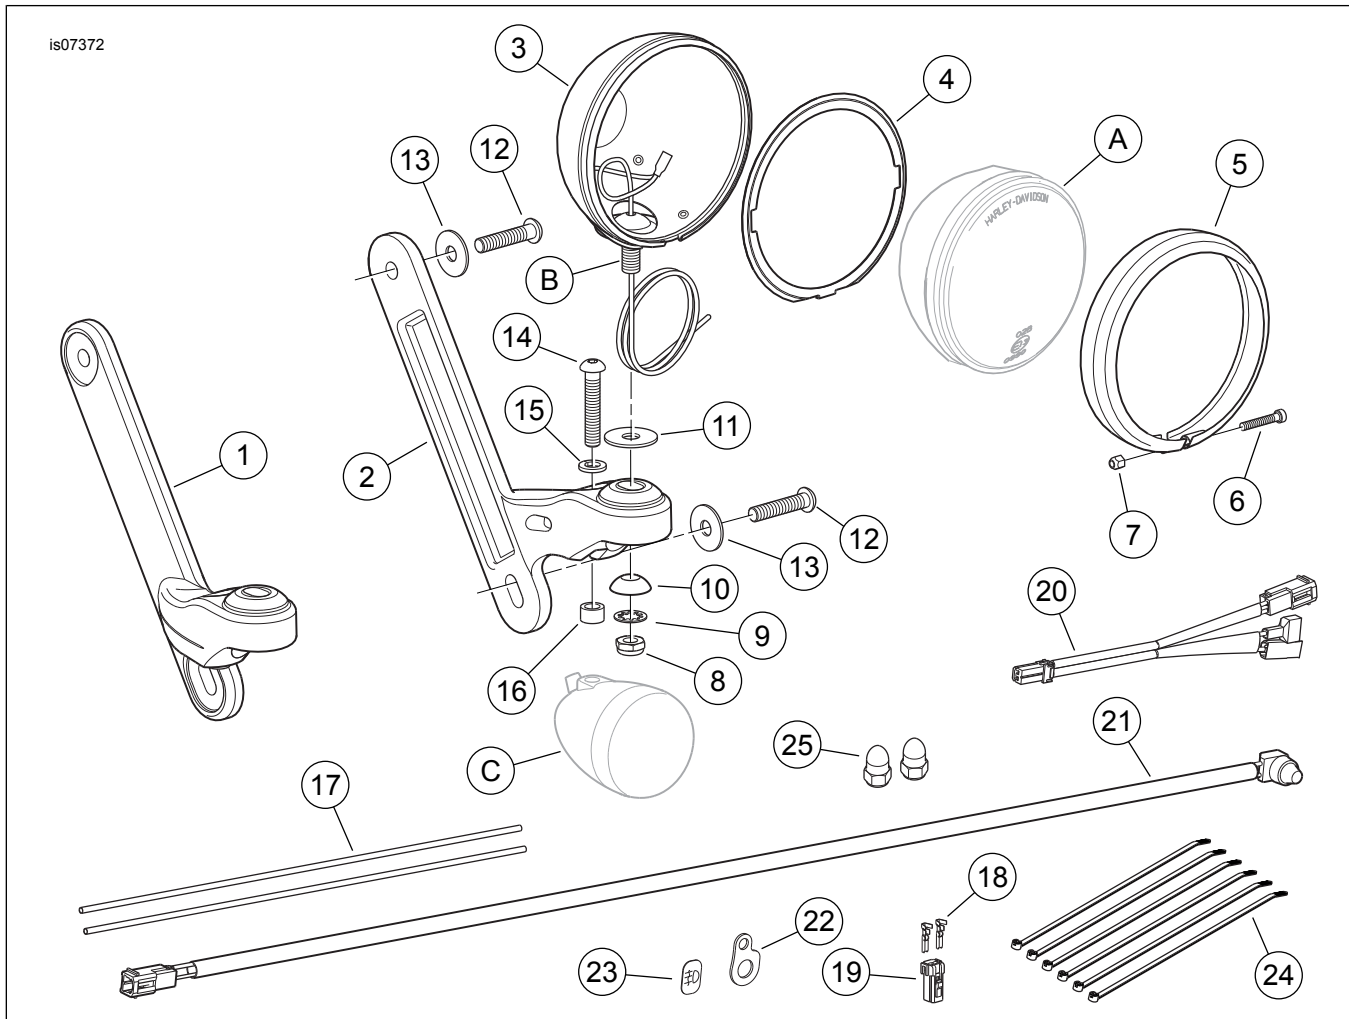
Pièces détachées, kit de montage de feu auxiliaire FLD
